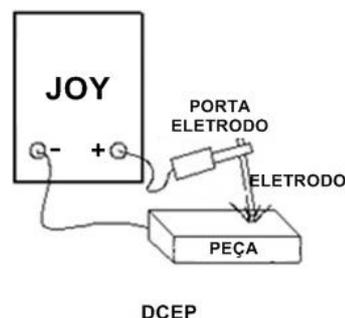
Conexão positiva para soldagem com eletrodo revestido
